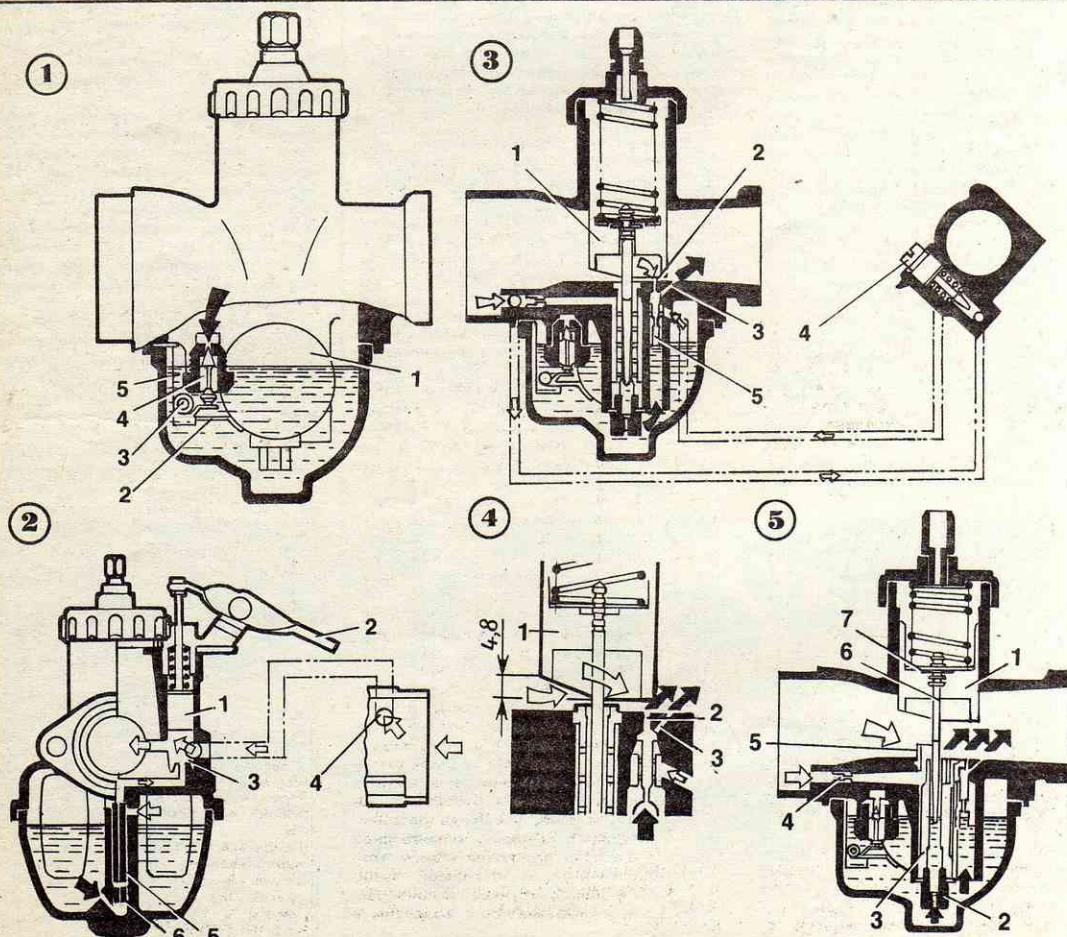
Поплавковый механизм: 1 — поплавок; 2 — рычаг; 3 — ось; 4 — игла; 5 — корпус клапана.
